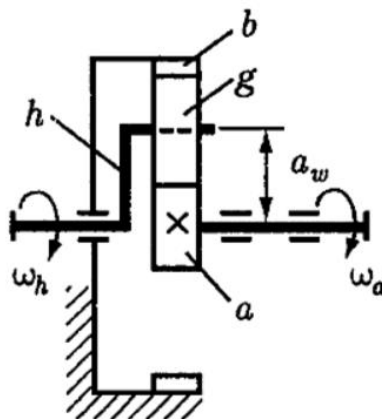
Кінемаїчна схема планетарного редуктора
